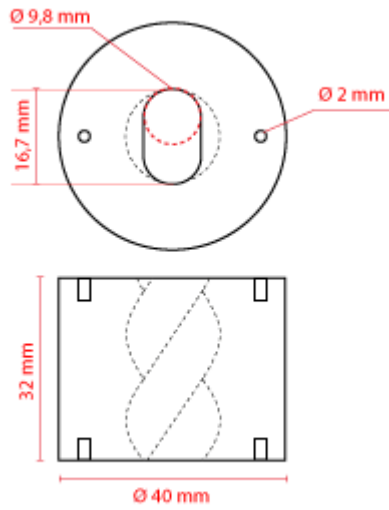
Desenho cotado do bico extrusor (peça "d")
